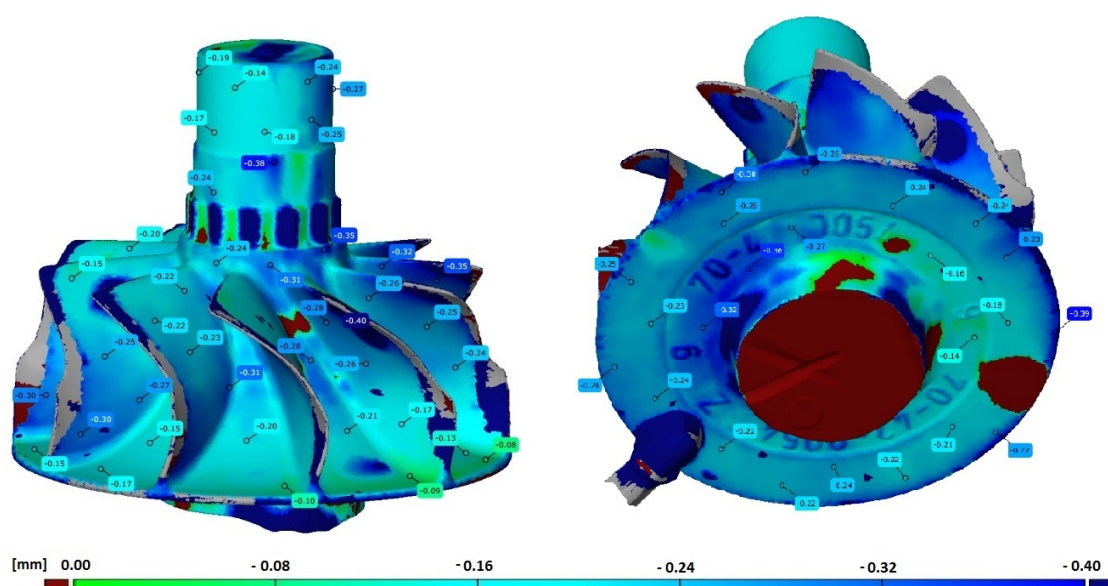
Sobreposição das geometrias das peças não maquinada e maquinada quimicamente durante 60 minutos
